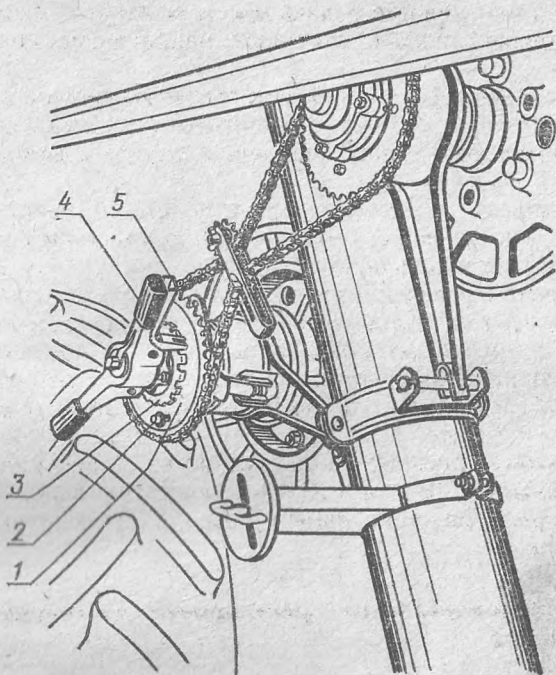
Регулировка натяжения ремня и оборотов барабана на двухбарабанных комбайнах:
